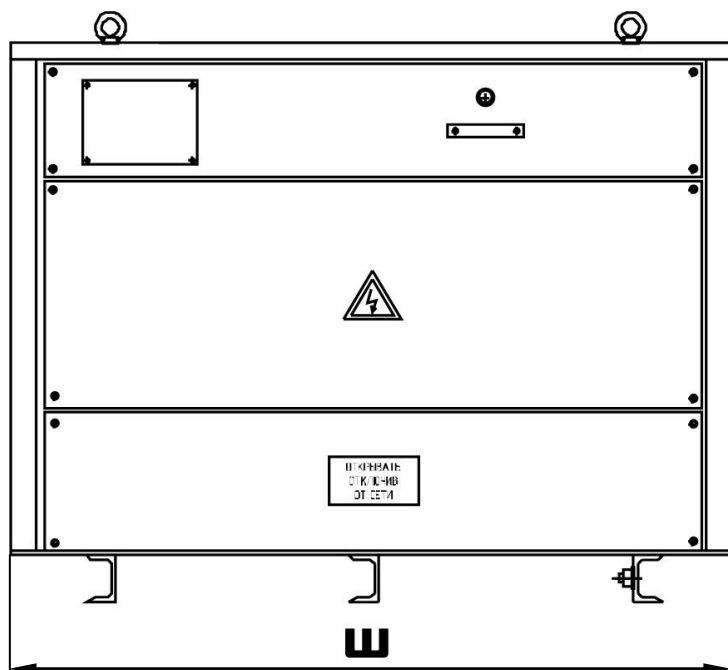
Внешний вид и габаритные размеры стабилизаторов типа СТС-3 АЭС
